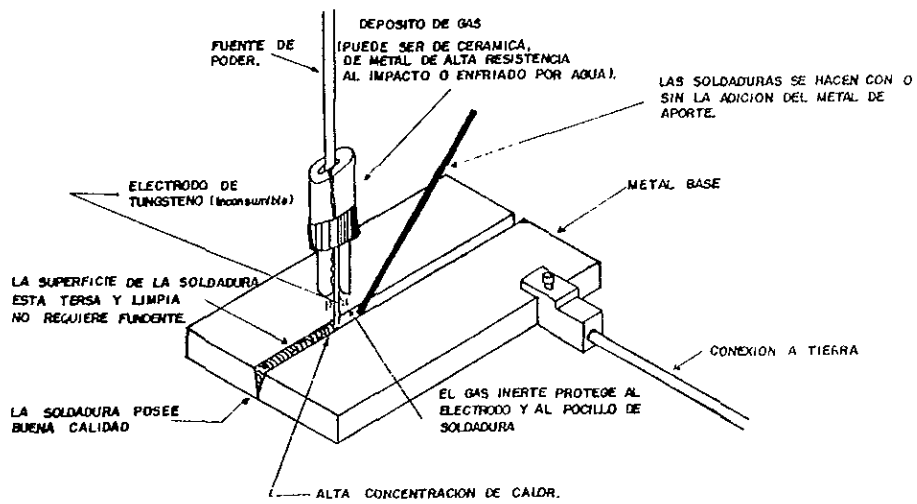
Soldadura de tungsteno y gas.
